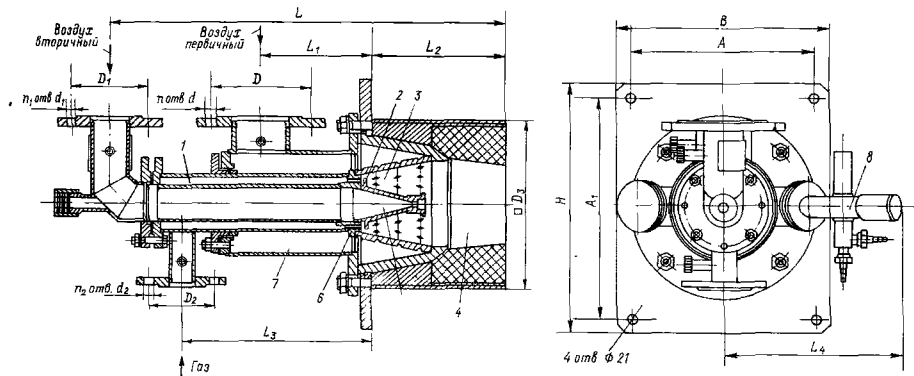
Горелка ГТГЦ конструкции ЦНИИТмаша.
